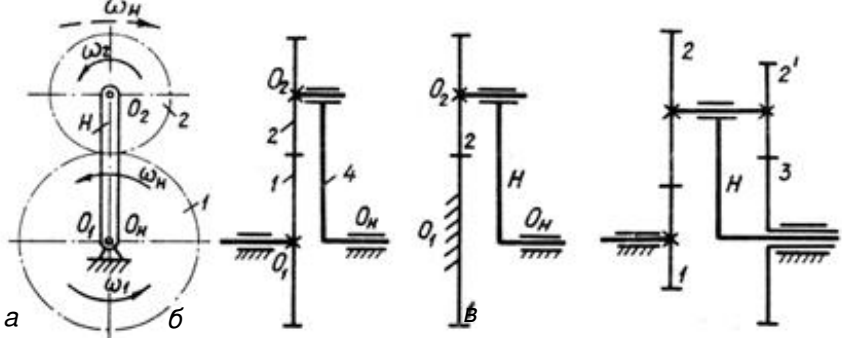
Зубчасті механізми з рухомими осями: а, в – диференціальні механізми; б – планетарний механізм
